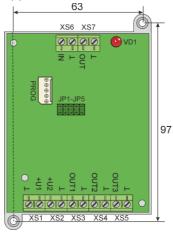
Внешний вид основания ис.1 Внешний вид крышки корпуса корпуса с установленной платой Назначение элементов модуля приведено в таблице 2.
